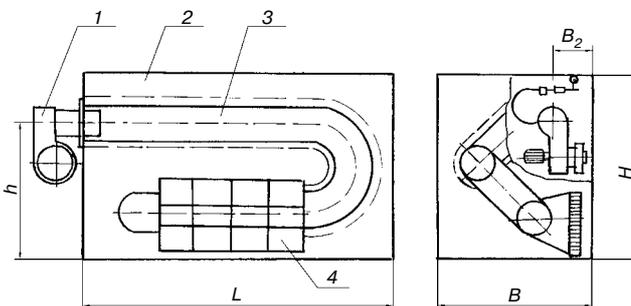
Схема ВГСК, основные конструктивные размеры: 1 – блочная горелка; 2 – корпус; 3 – теплообменник; 4 – каталитическая поверхность
